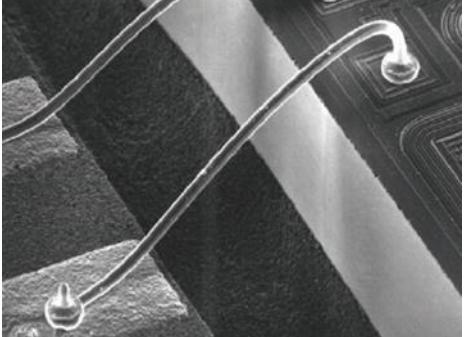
Профиль проволочного контакта, выполненного по технологии термозвуковой сварки «шарик-клип»
